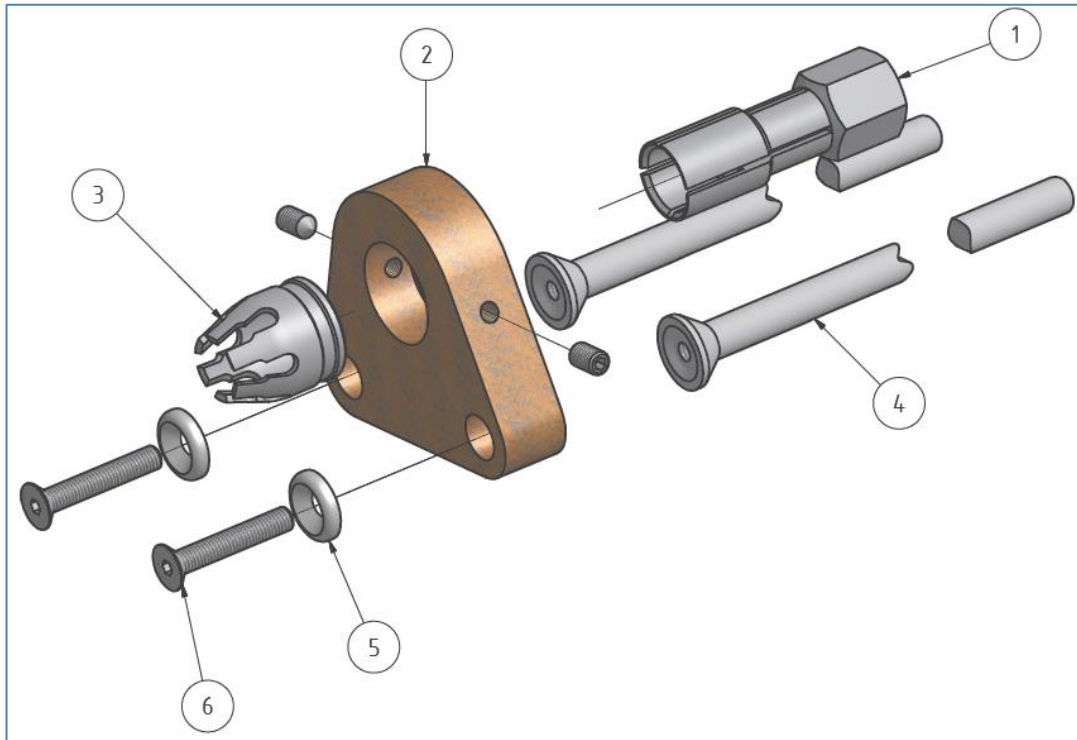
Stützeinrichtung für Gewindebolzen, Innengewindebuchsen und glatte Stifte
